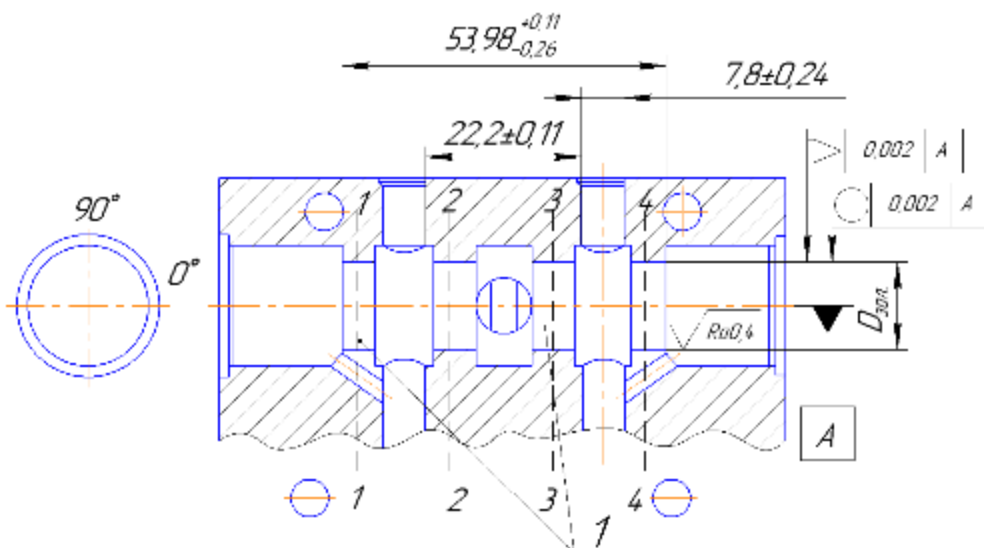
Схема виміру отвору корпусу клапанної коробки
